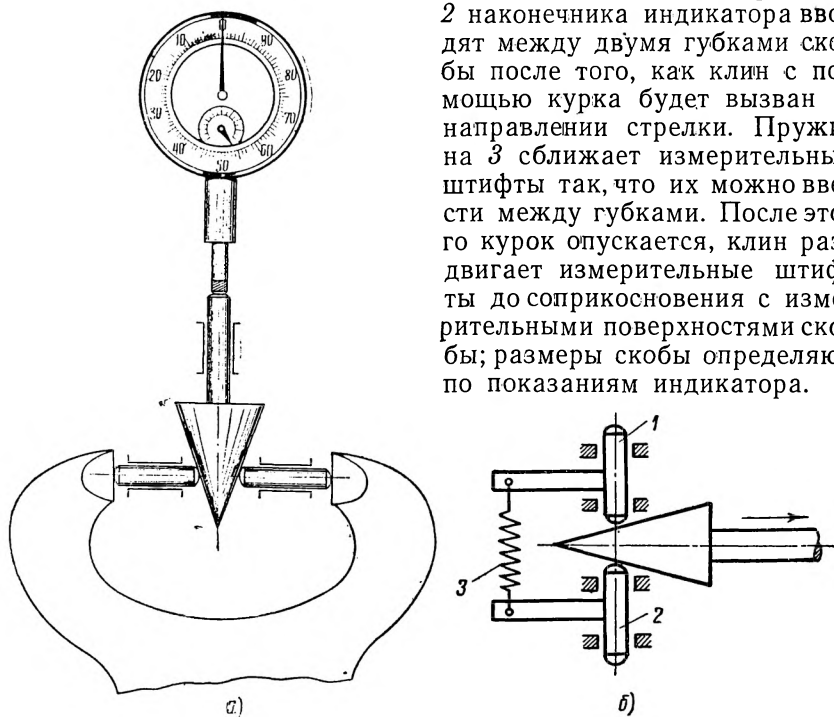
Двухконтактный индикатор для измерения внутренних размеров:
